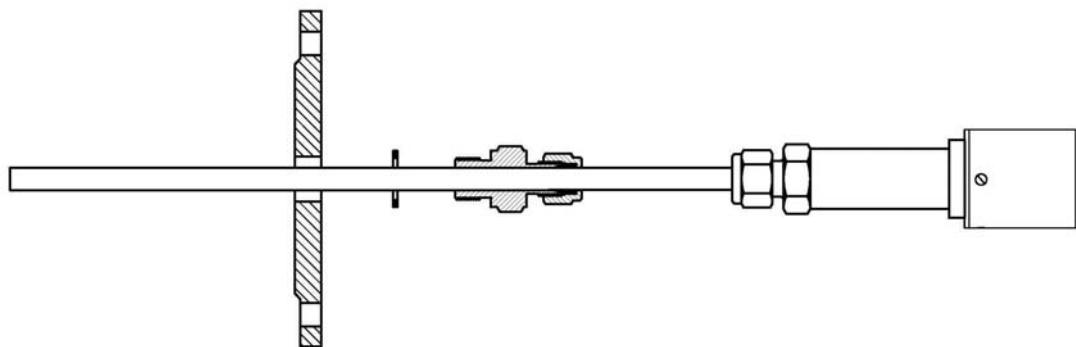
Установка штуцера установочного на измерительный элемент
